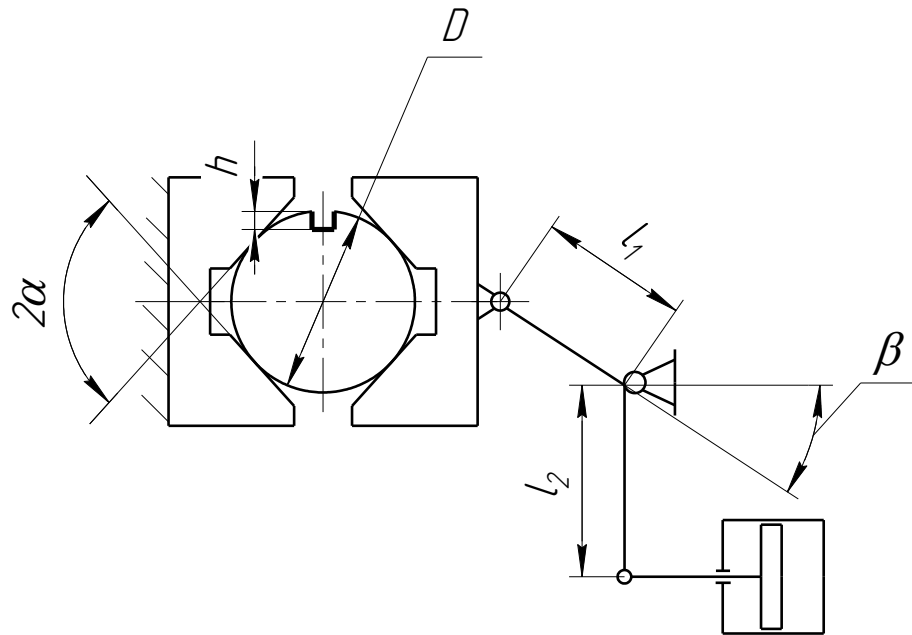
Принципова схема механізованого пристосування для фрезерування шпонкового пазу кінцевою фрезою
